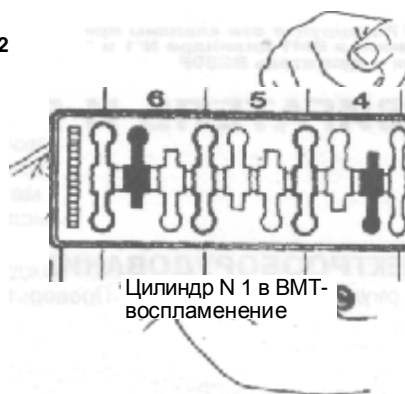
При регулировке клапанов метка зажигания на шкиве должна совпадать с отметкой "O" на блоке двигателя — двигатель B280F
